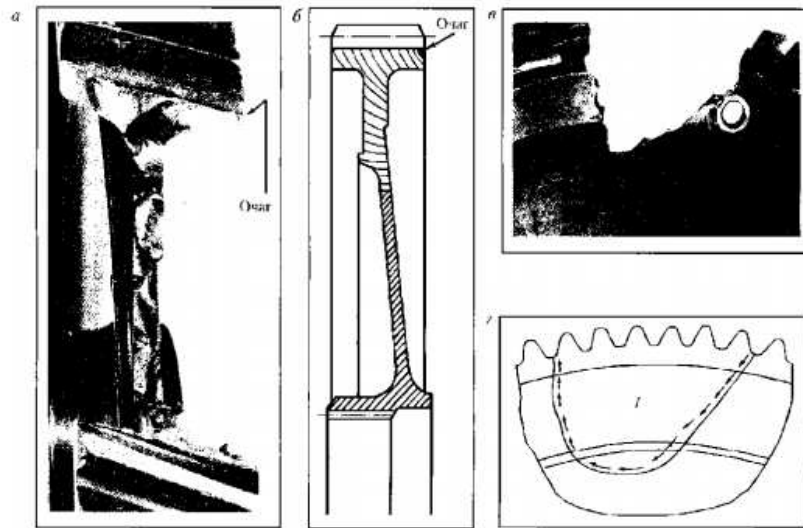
Загальний вигляд (а) зруйнованого (в) зубчастого колеса вертольота Ми-8 (б), схема розповсюдження в ньому тріщини (г)
